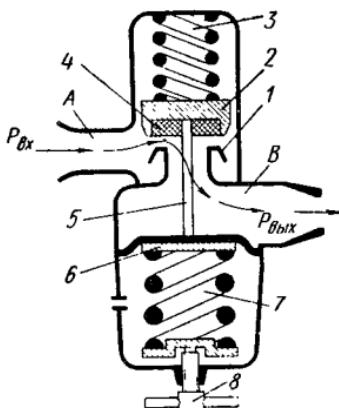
Схема одноступенчатого газового редуктора с механическим заданием рабочего давления
